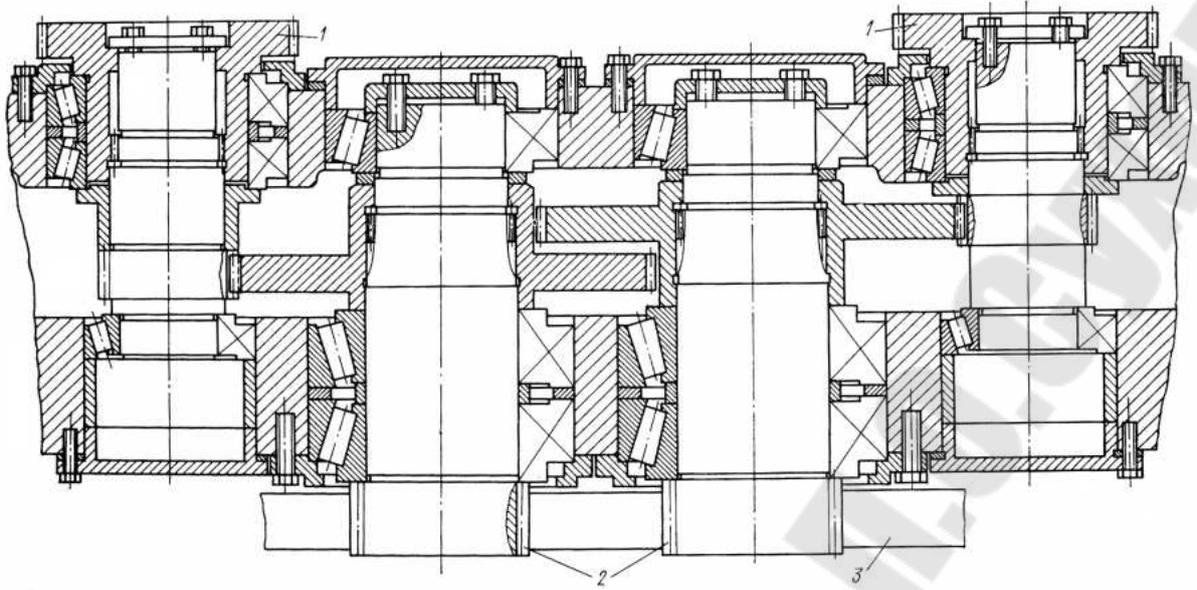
Выходное звено привода подачи фрезерного станка 6Б445Ф3 с зубчатой реечной передачей:
